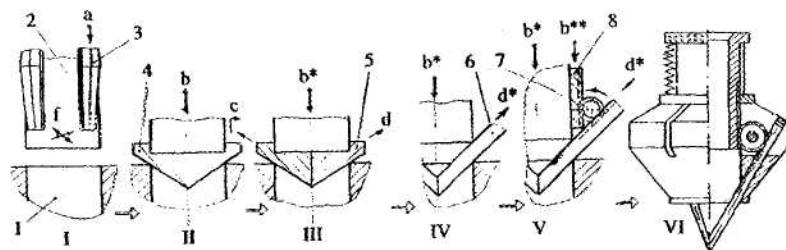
Схема процесу формування конструкторського інноваційного рішення – орієнтуочного складального модуля для деталей типу валик–втулка
